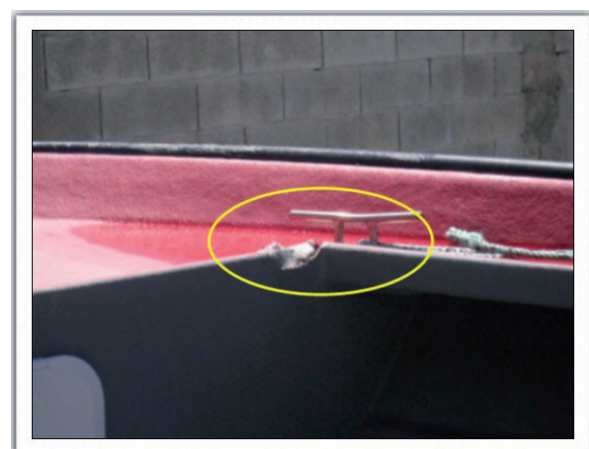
Daños en la cubierta de la embarcación CIMA, en la proa en estribor. Fotografía sacada desde la popa en babor
